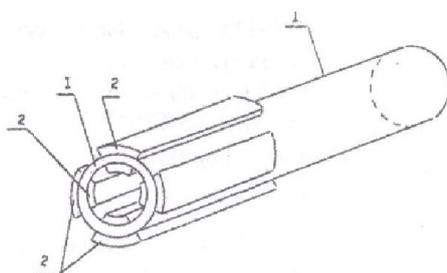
Направляющая труба токарного автомата с трапециевидными неметаллическими демпфирующими элементами модели МН-1-[3]
